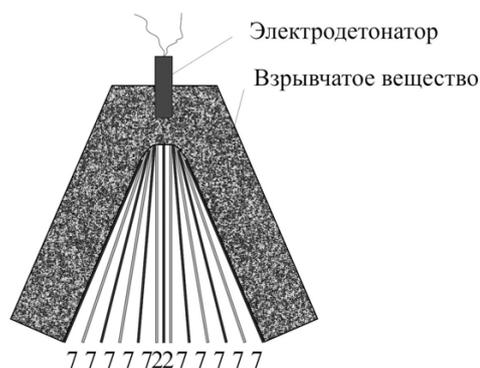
Схема сварки взрывом стальных пластин. Цифры соответствуют величине зазоров между чередующимися пластинами
